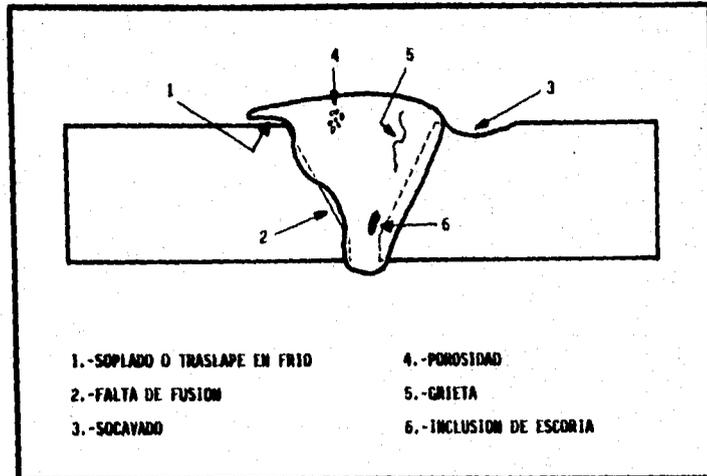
DEFECTOS TÍPICOS EN UN DEPÓSITO DE SOLDADURA.
